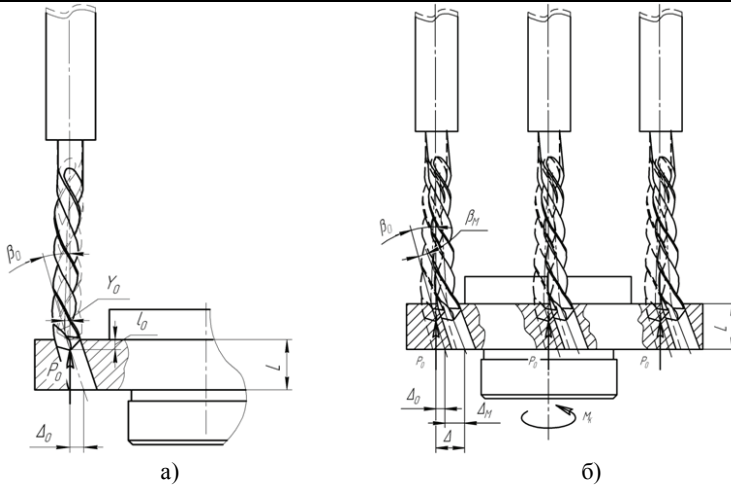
Схеми формування величини відведення сверд: а – при одноінструментній обробці; б – при обробці багатшпindelною головкою для токарного верстата
